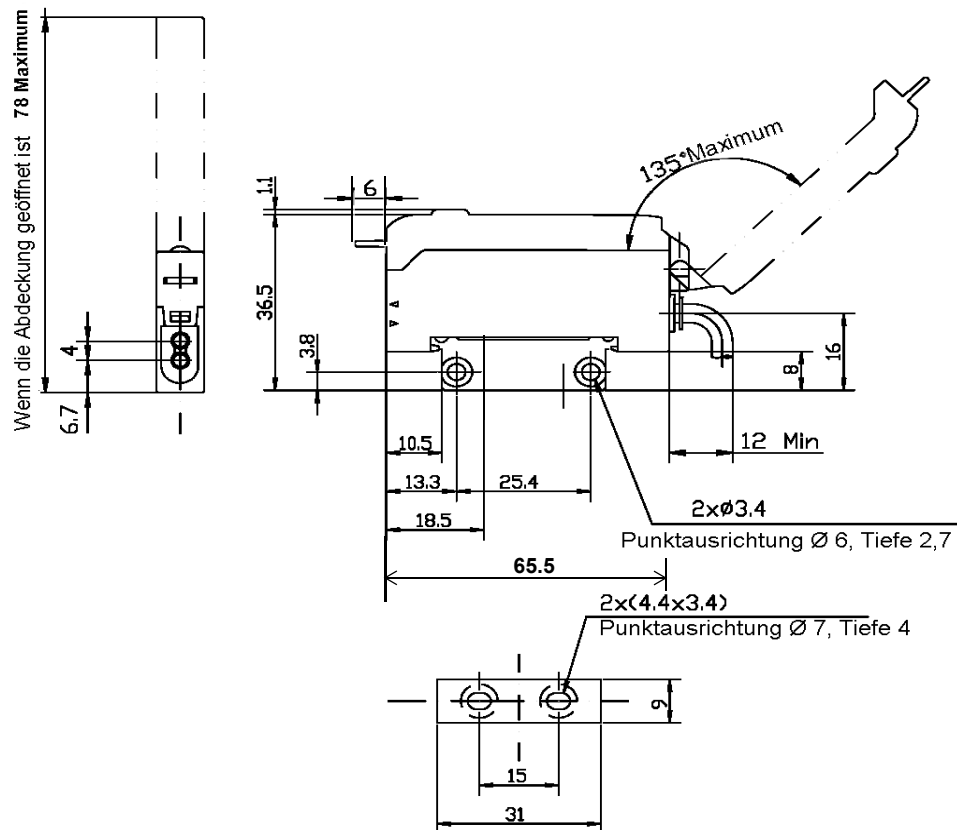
Fotozelle mit Installationsmontage – Abmessungen
